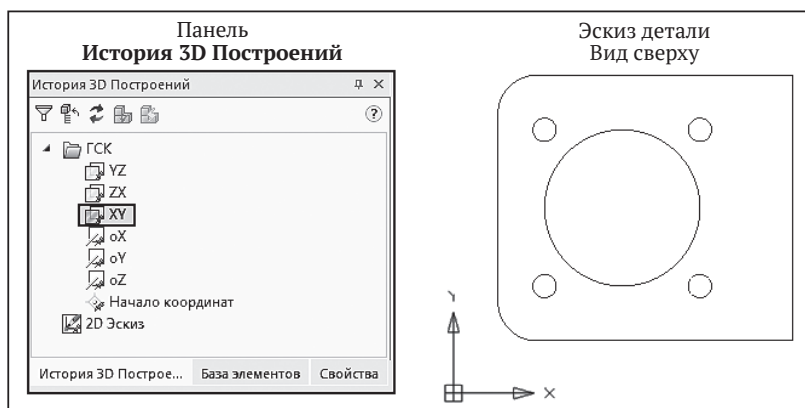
Эскиз вида сверху детали «Скоба»
